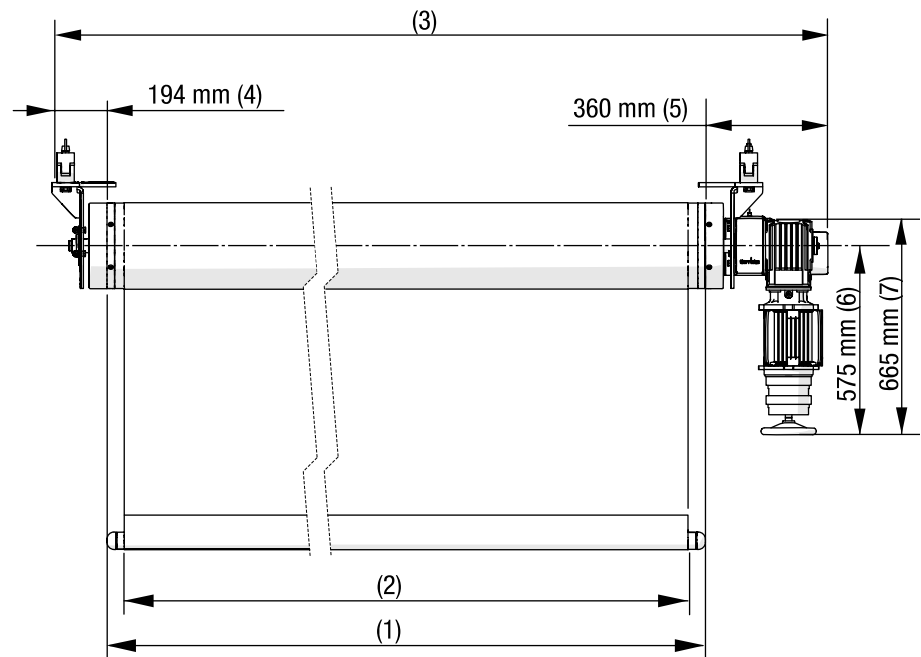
Rollbildwand TUBE – Maße Frontalansicht
